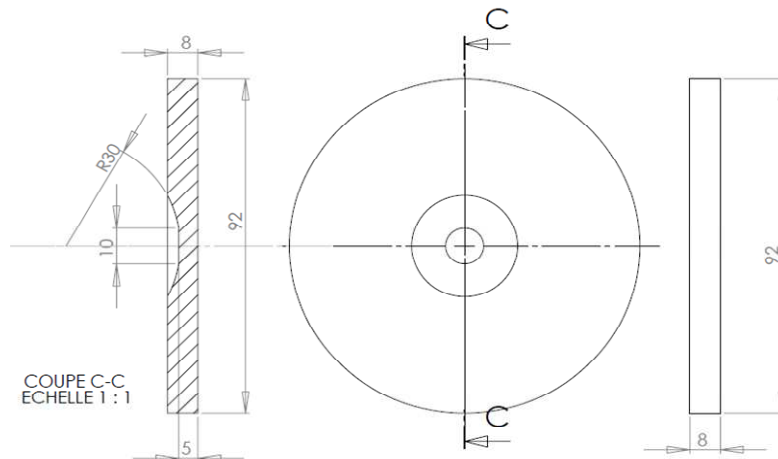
Géométrie de l'éprouvette disque pour l'AlSi7Cu05Mg03
